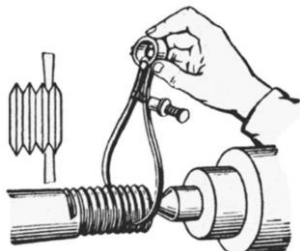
Вимірювання внутрішнього діаметра різьби кронциркулем із гострими ніжками
